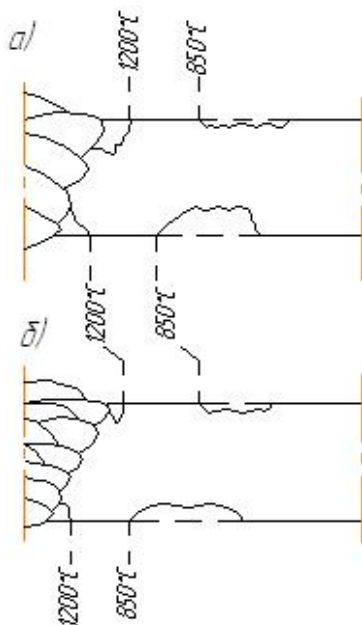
Схема коррозионного разрушения сварного соединения из стали 08X18Н10Т в растворе азотной кислоты: а) сварка «толстыми» валиками без охлаждения; б) сварка «тонкими» валиками с охлаждением [2]
